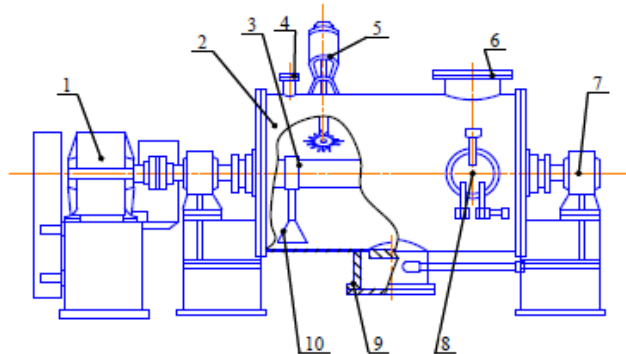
Плужковий змішувач типу СПЖ-500: 1 – електродвигун; 2 – корпус змішувача; 3 – вал; 4 – штуцер; 5 – електродвигун; 6 – завантажувальний патрубок; 7 – корпус підшипника; 8 – люк; 9 – вивантажувальний патрубок; 10 – лопаті.
